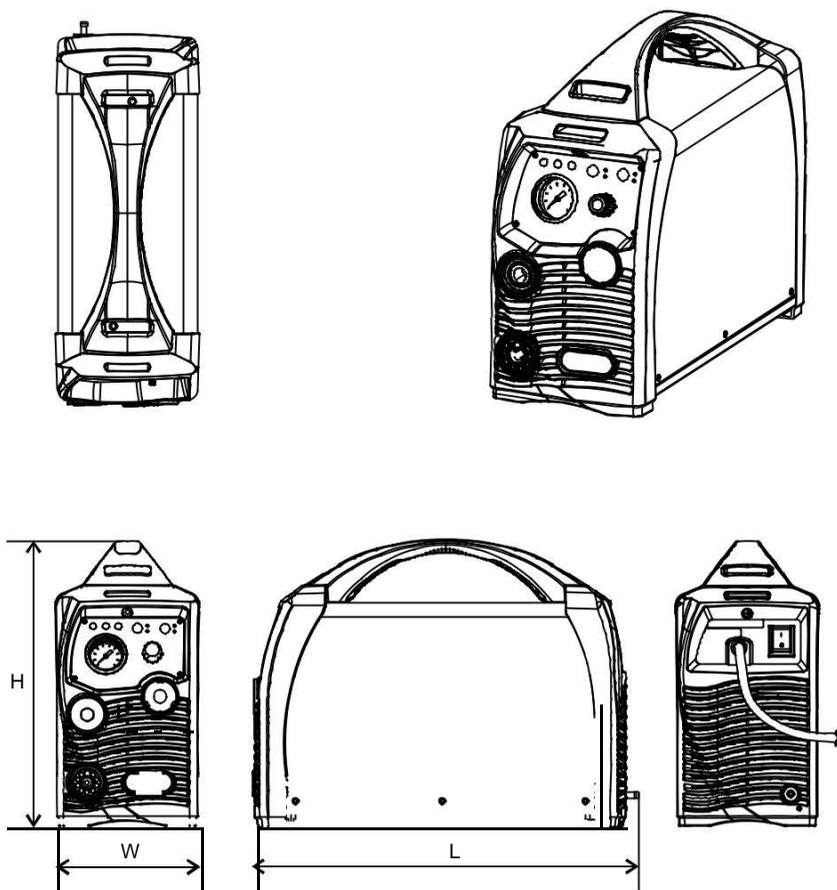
Aspetto e dimensioni della macchina (Unità: mm)
